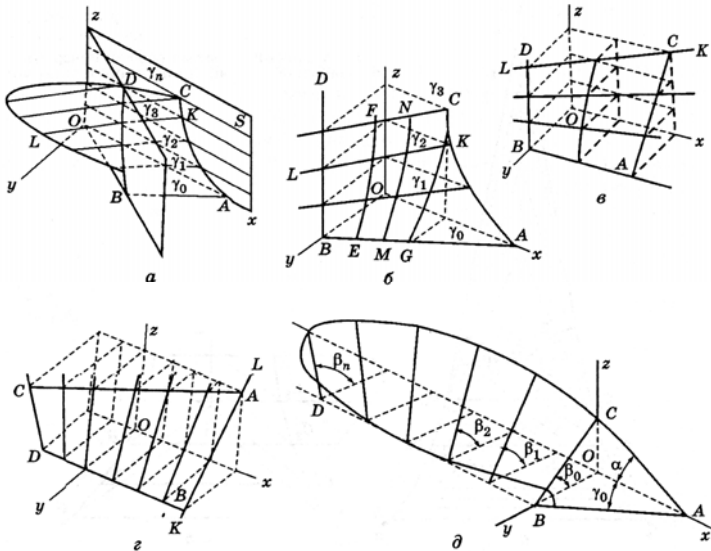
Розвиток косою тригранного клина в циліндричну робочу поверхню: а – утворення ламаної робочої поверхні; б – побудова робочої циліндричної поверхні
